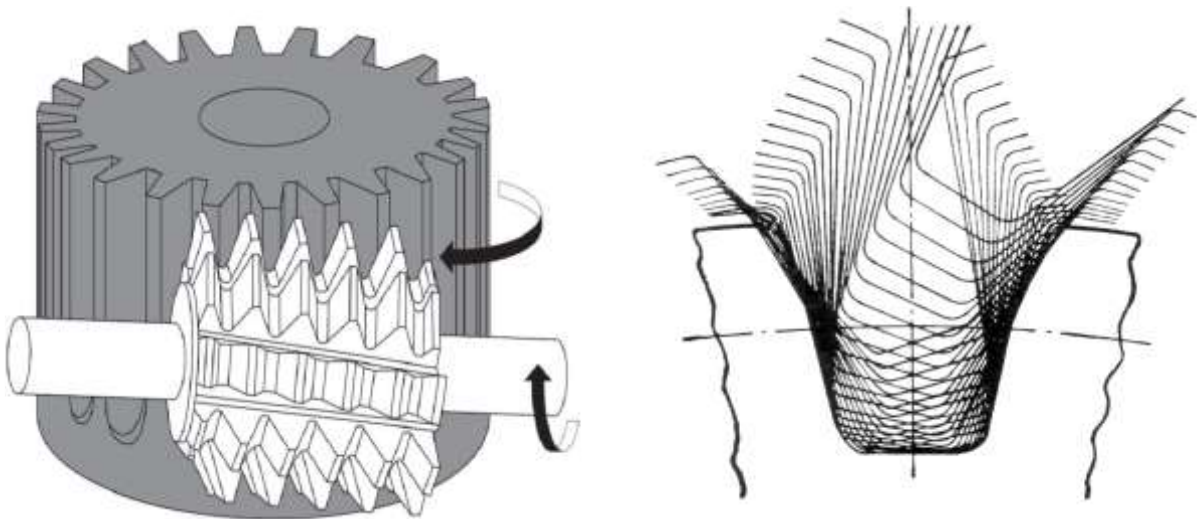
Формотворення евольвентного профілю циліндричного зубчастого колеса черв'ячною фрезою
